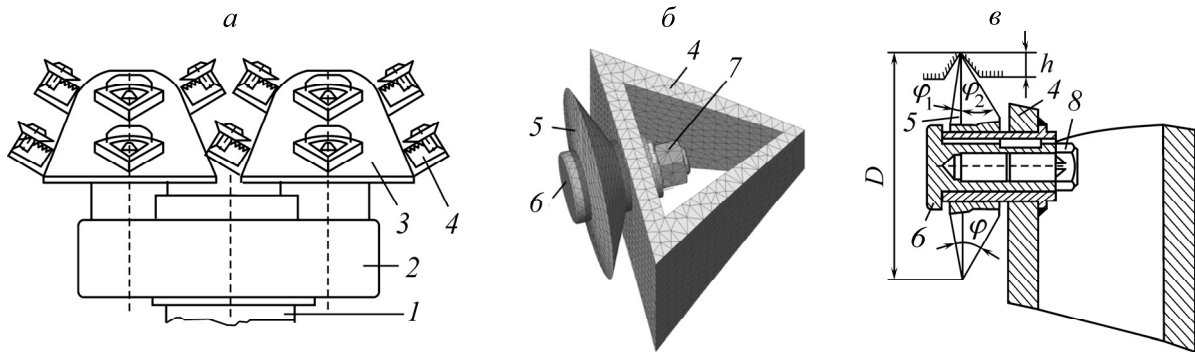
Исполнительный орган с двумя радиальными разрушающе-погрузочными коронками и дисковыми инструментами на трехгранных призмах: *а* — конструктивная схема; *б* — конечно-элементная модель консольного узла крепления дискового инструмента гайкой; *в* — конструкция узла крепления винтом: 1 — стрела; 2 — раздаточный редуктор; 3 — коронка; 4 — трехгранная призма; 5 — диск; 6 — ось; 7 — гайка; 8 — винт
